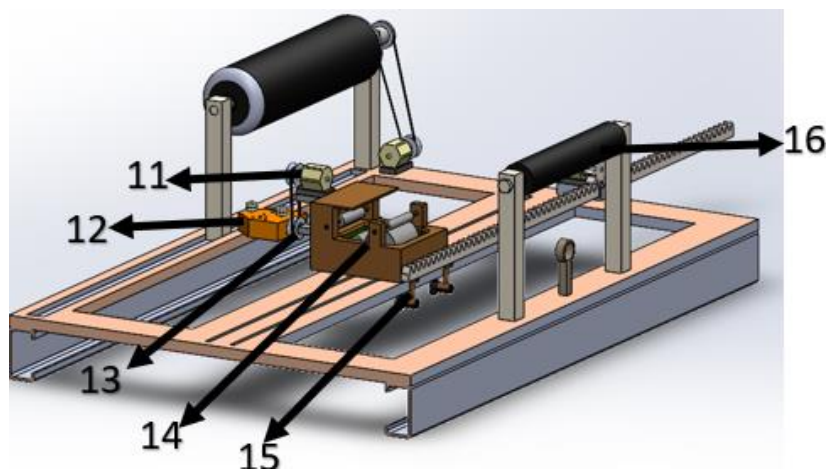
Diseño final máquina FILAMENT WINDING. Autor
